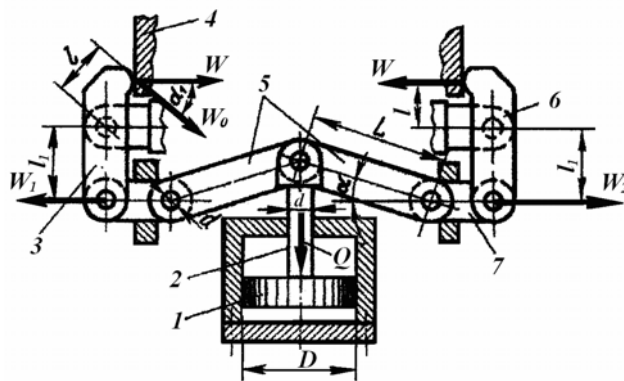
Конструктивная схема двухрычажного шарнирного механизма-усилителя двустороннего действия без плунжера
